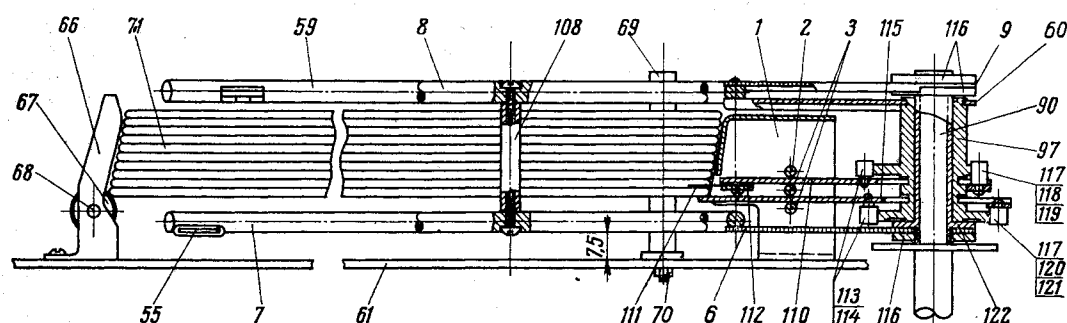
Механизм смены пластинок: 1 — кронштейн; 2, 3 — направляющие валики; 6 — пластина нижнего ухвата; 7 — нижний ухват; 8 — верхний ухват; 9 — пластина верхнего ухвата; 55 — держатель нижний; 59 — поворотная часть верхнего ухвата; 60 — пластина; 61 — панель; 66 — кронштейн; 67 — ролик; 68 — ось ролика; 69 — упор левый; 70 — гайка М4; 71 — пакет грампластинок; 90 — ведущий вал; 97 — блок кулачков; 108 — стойка; 110 — верхний нож; 111 — пластина верхнего ножа; 112 — накладка; 113, 118, 120 — ролики; 114, 119, 121 — оси роликов; 115 — нижний нож; 116 — гайки; 117 — пластины; 122 — втулка.
